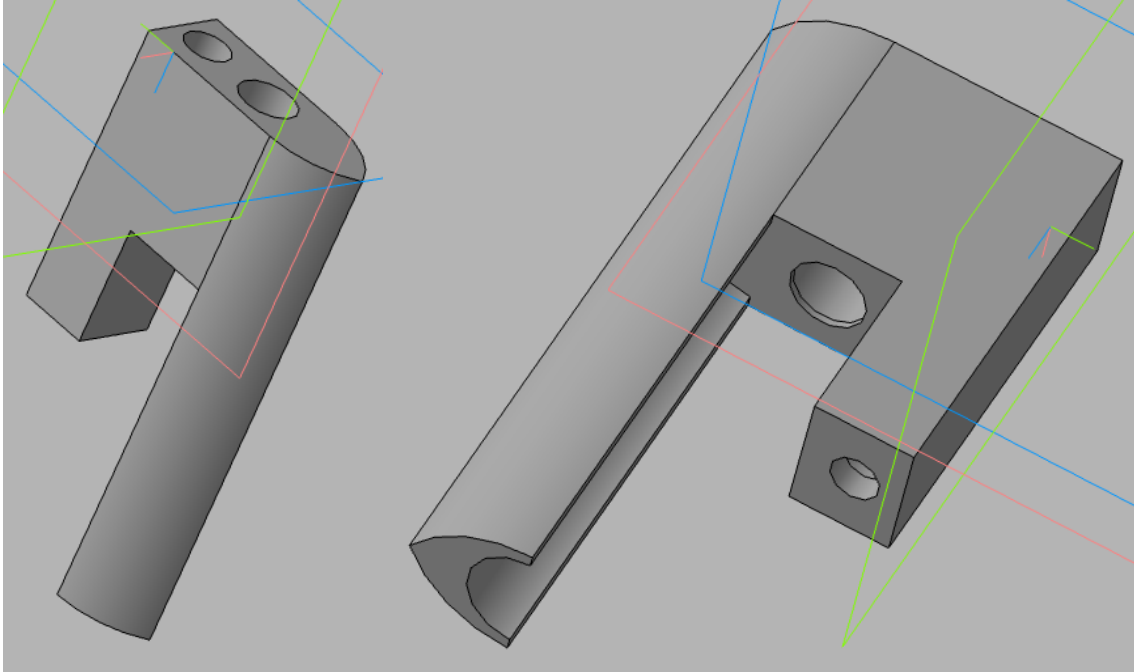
Загальний вигляд корпусу одного модуля.
